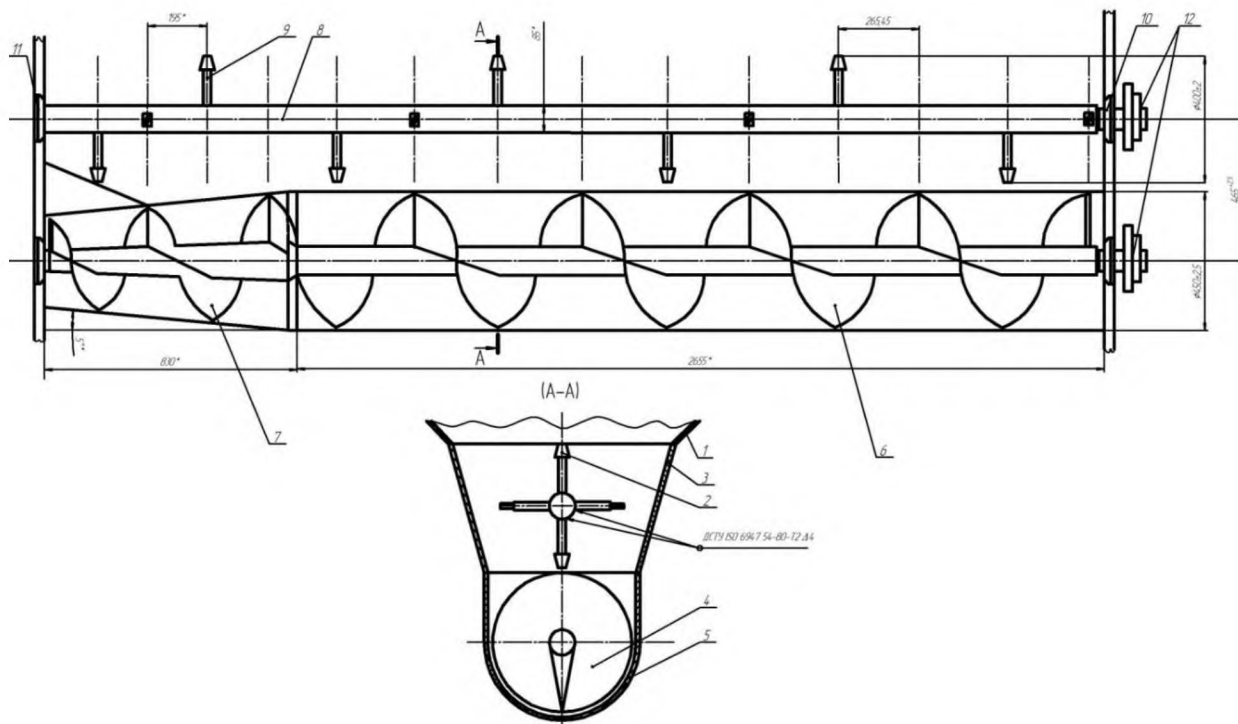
Конструктивне компонування механізму внесення органічних добрив: 1- секція бункера; 2- розрихлювач; 3- конусний корпус; 4- шнек; 5- корпус шнека; 6- циліндрична частина шнека; 7- конічна частина шнека; 8- вал розрихлювача; 9- зубові лопатки; 10 і 11- підшипникові вузли; 12- блок зірочок
